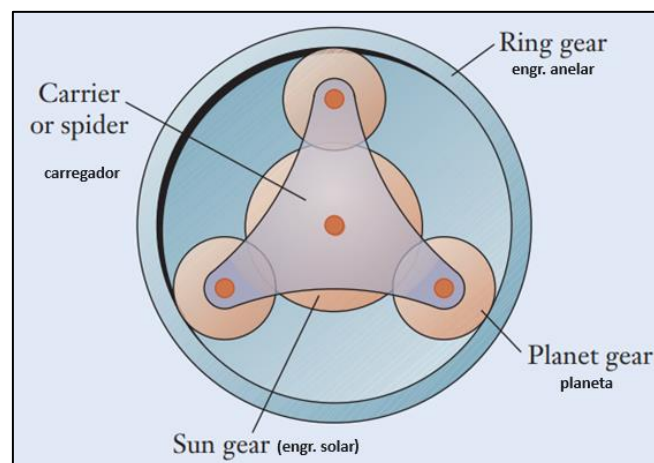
Arranjo das engrenagens planetária (fonte:[1])
